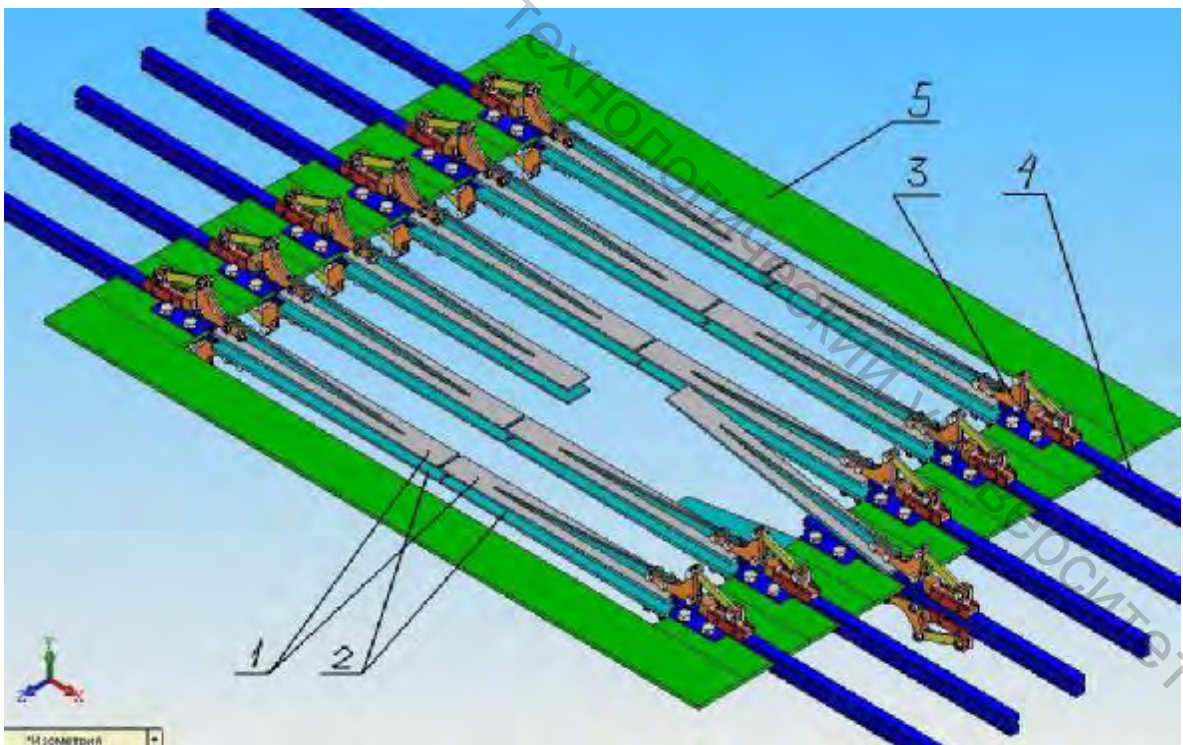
Общий вид устройства фиксации деталей обуви
